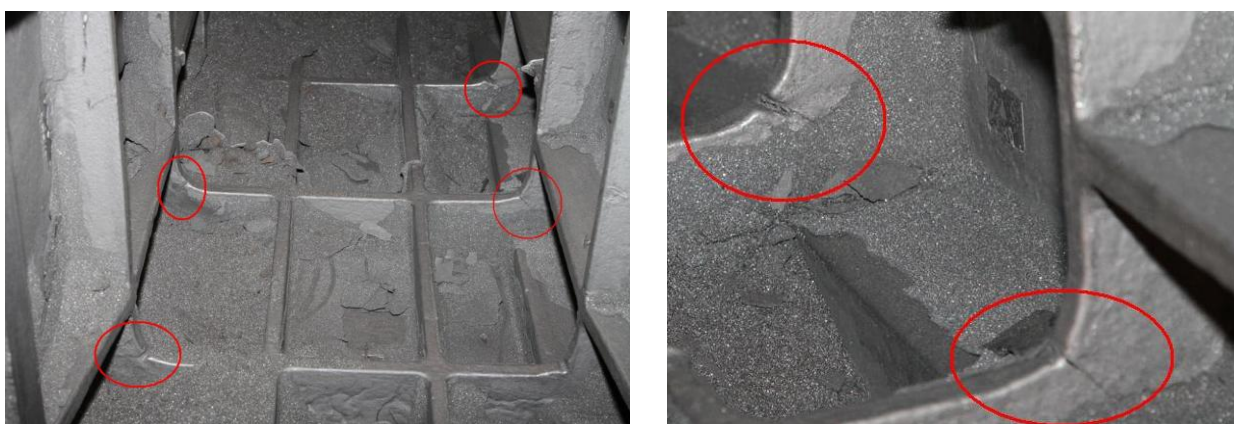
Трещины, образующиеся на внутренних ребрах жестки отливки «Колонна»
